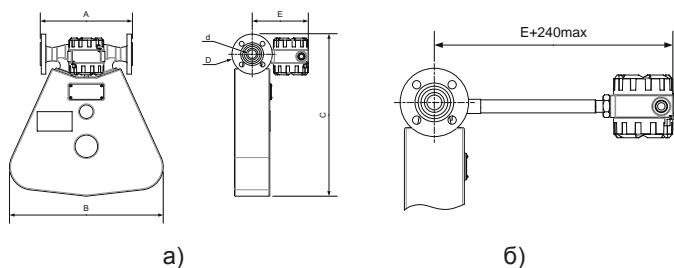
Габариты и присоединительные размеры датчиков Ду25...80:
